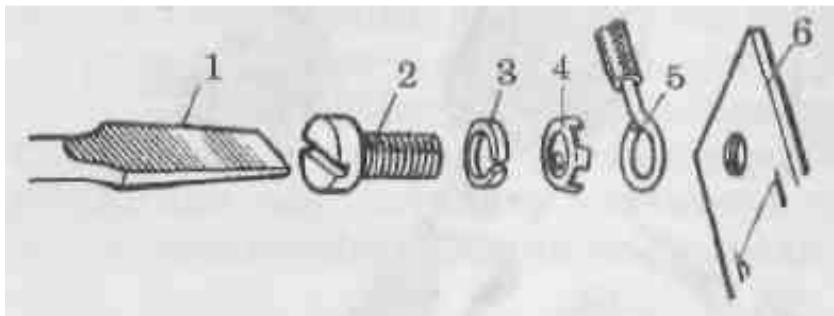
Присоединение алюминиевой жилы к плоскому выводу электрического аппарата: 1 – отвертка; 2 – винт; 3 – пружинная шайба; 4 – шайба-звездочка; 5 – алюминиевая жила; 6 – контактный вывод
